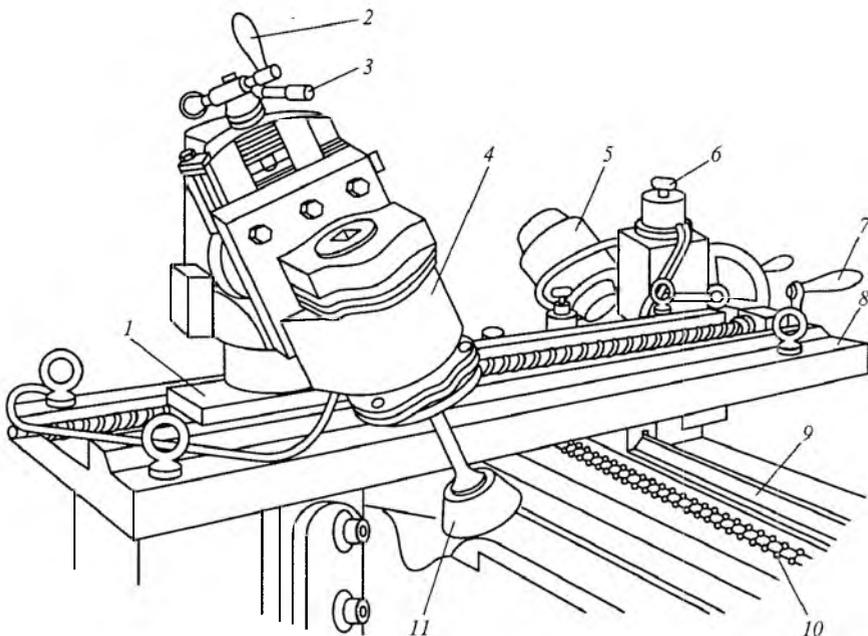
Самодвижущаяся шлифовальная головка:
